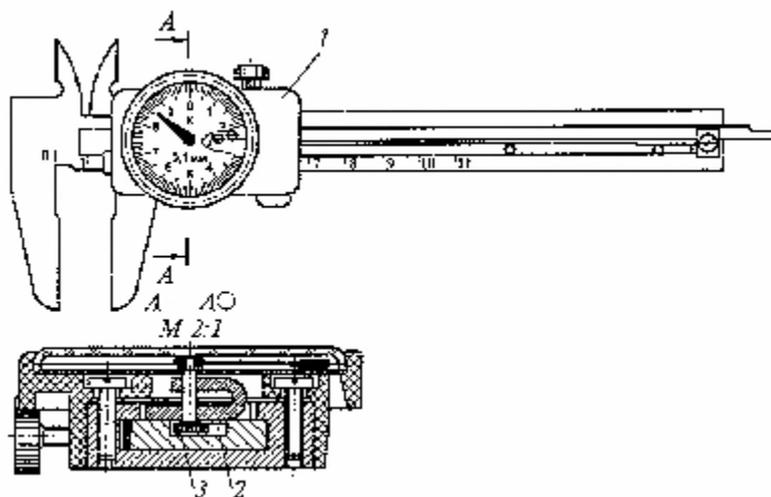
Конструкция индикаторного штангенциркуля: 1 – рамка; 2 – зубчатая рейка; 3 – зубчатое колесо
